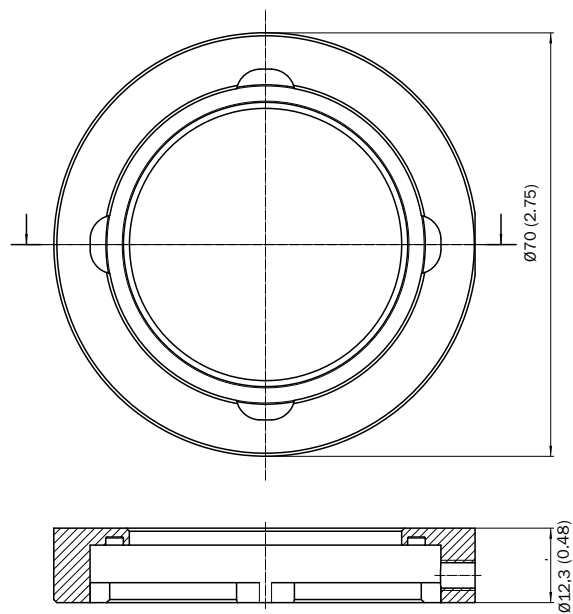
Adapterflansch Klemmflansch DIN32676 3"/DN65, geeignet für PS= 10 bar (150 psi)
